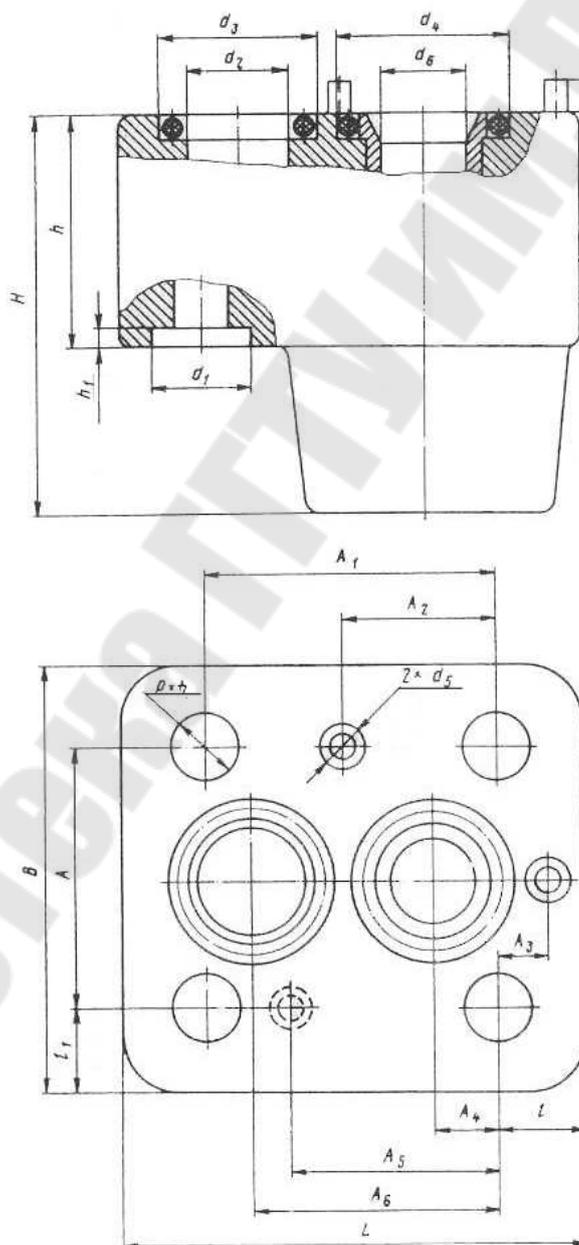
Габаритные и присоединительные размеры гидроклапанов
